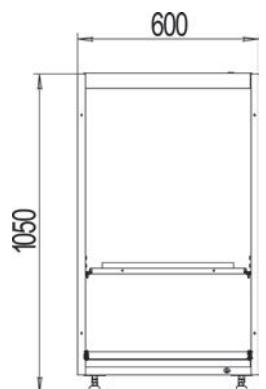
Габаритный чертеж стеллажа аккумуляторного 1050x600x600
